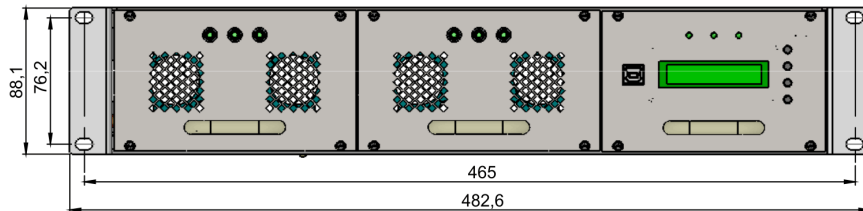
Габаритные размеры BC24/70-2/2
